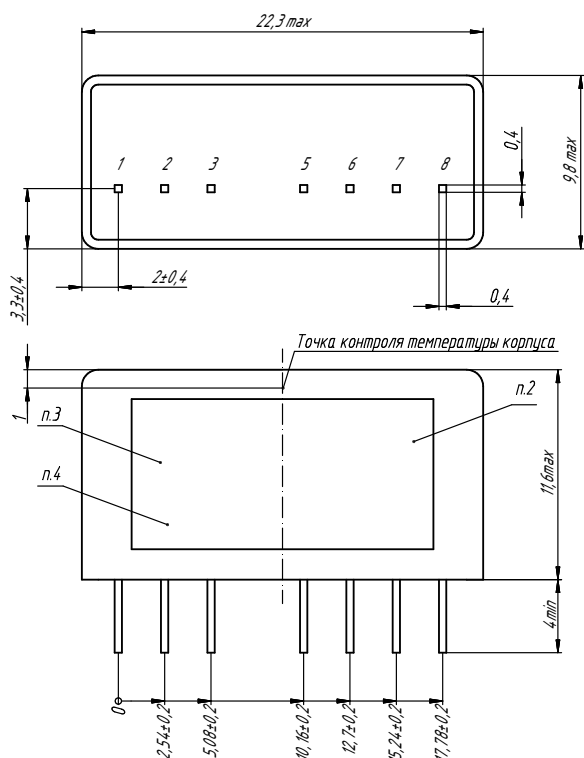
Габаритный чертеж для VDN2, VDN5.
